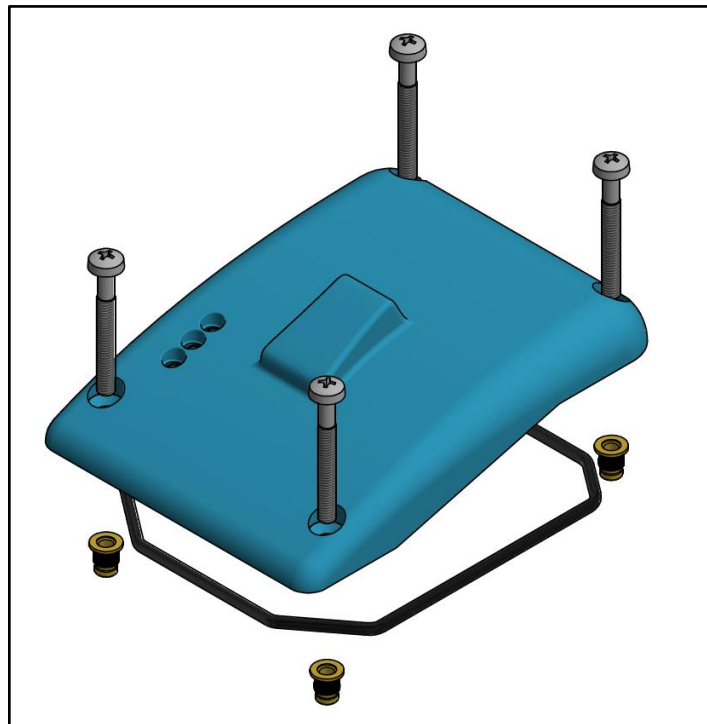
Vista isométrica de la tapa superior más o-ring, tornillo e insertos.
